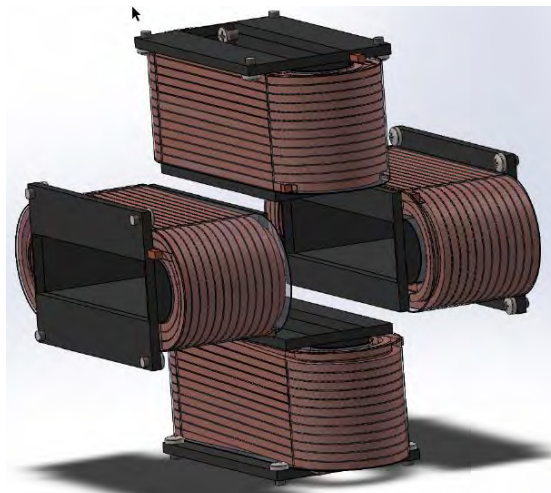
Vedere CAD 3D a ansamblului de bobine cvadripolare.
